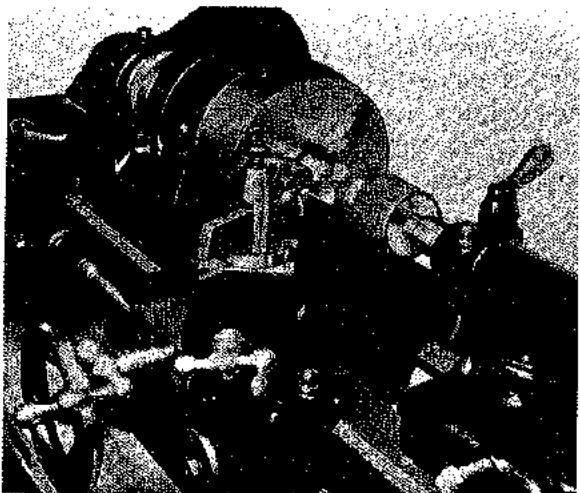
Disposición para el taladrado de centros en una pieza pequeña (South Bend Lathe Works).
